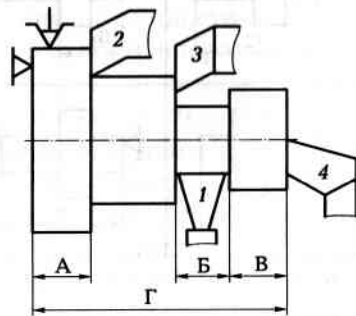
Схема обработки на токарно-револьверном станке:
